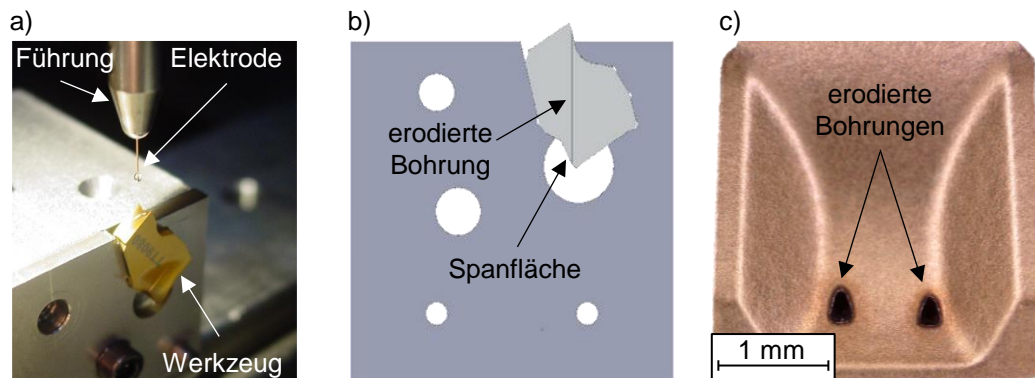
Modifiziertes Werkzeug; a) montiert in der Erodieranlage; b) 2D-Modell der Vorrichtung mit Werkzeug; c) erodiertes Werkzeug
